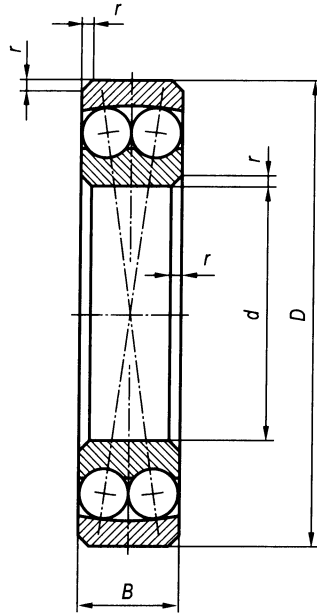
Подшипник шариковый радиальный сферический двухрядный серий 1200, 1300, 1500 и 1600
